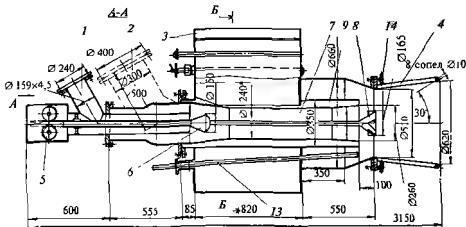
Горелка ВНИИМТ для совместного сжигания природного и ферросплавного газов в трубчатых печах.
